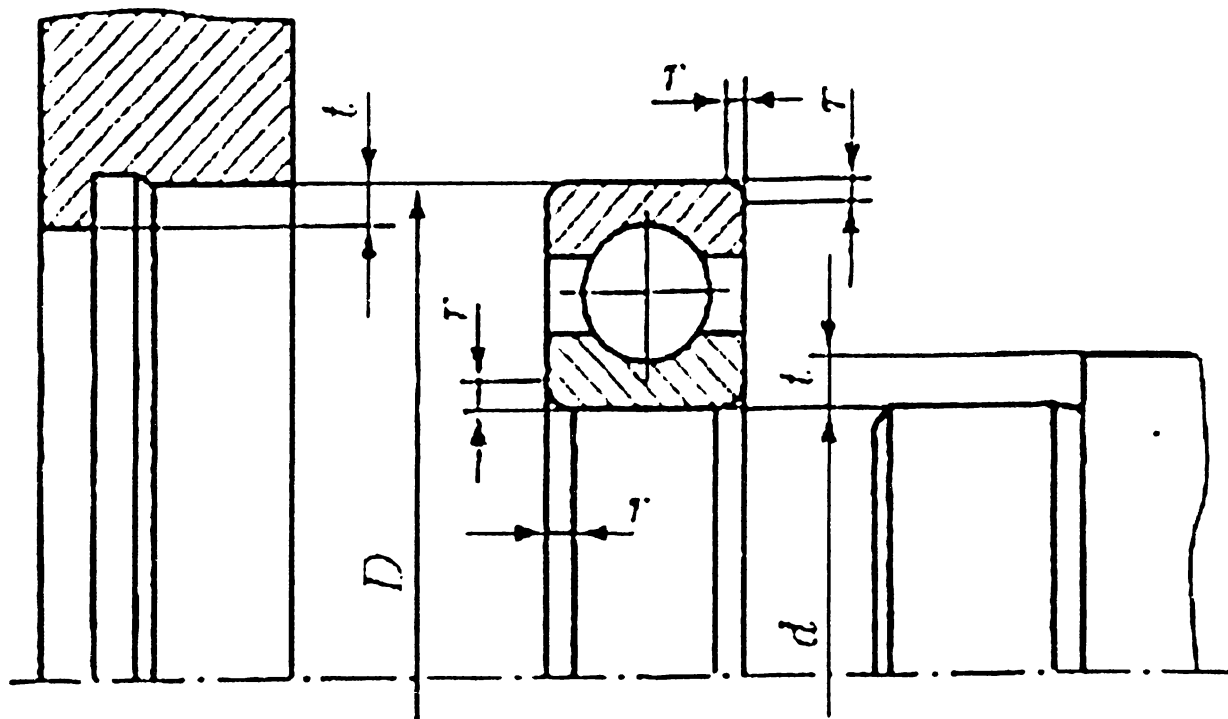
Буртики (заплевички) на валу и в отверстии корпуса для упора колец подшипников
